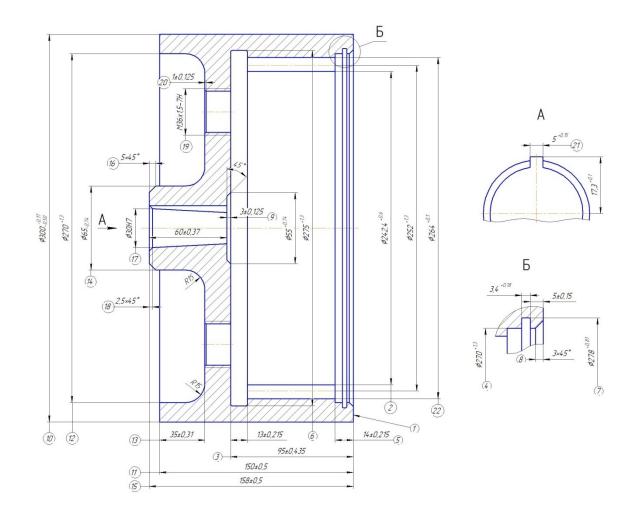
Обрабатываемые поверхности детали "Корпус муфты"
